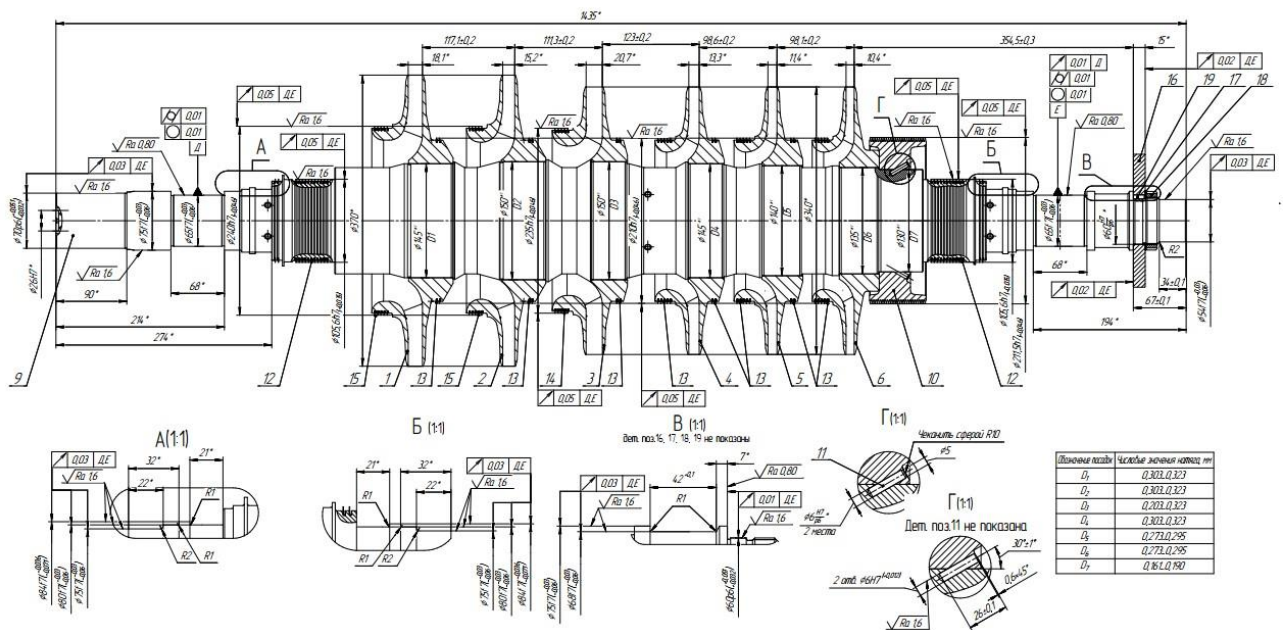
Креслення вузла ротора С-102 ЦВД
